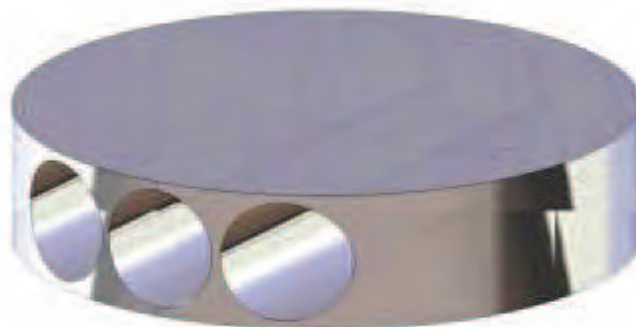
Carottage de trois cylindres par pastille Ø36h8mm pour l'usinage des éprouvettes
